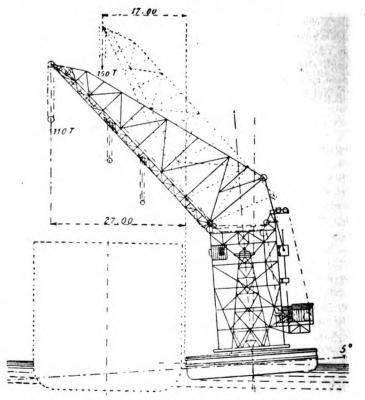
Gru galleggiante da 150 tonn. dei Cantleri Harland - Elevazione
